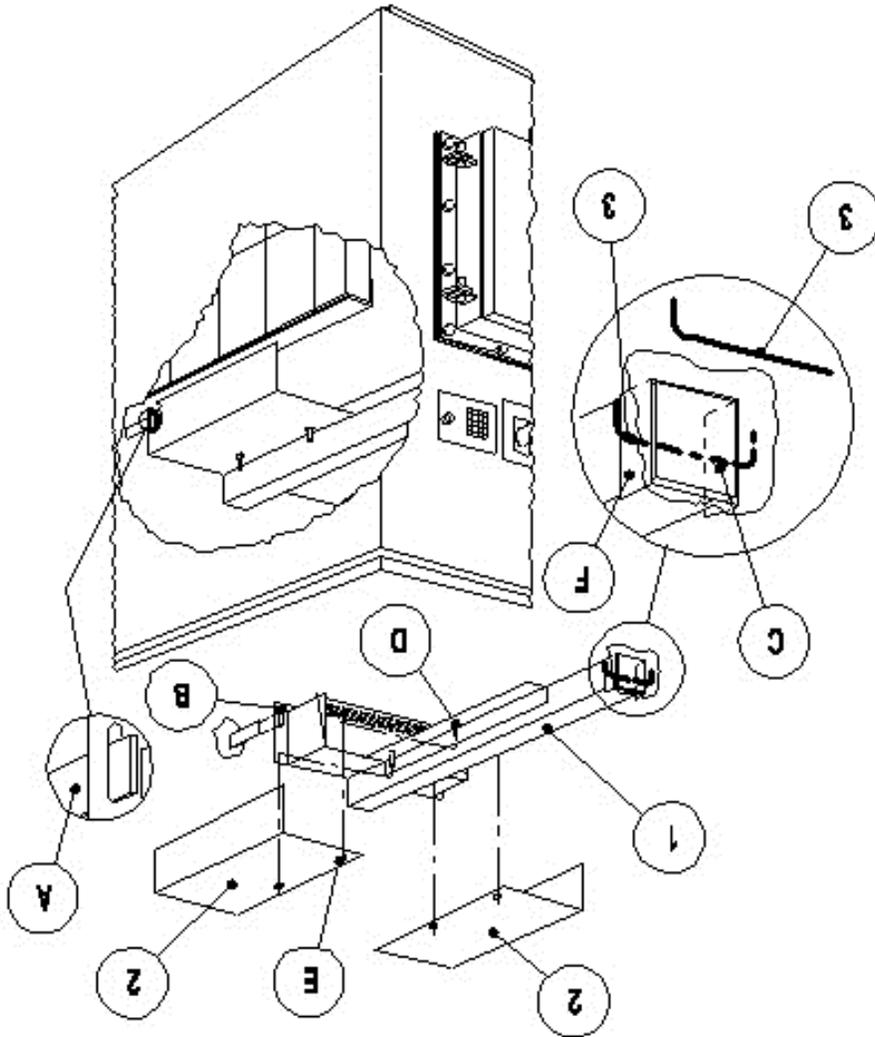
ÉTAPES POUR L'ENLÈVEMENT OU L'INSTALLATION DE LA CHICANE ET DU SYSTÈME D'AIR SECONDAIRE
